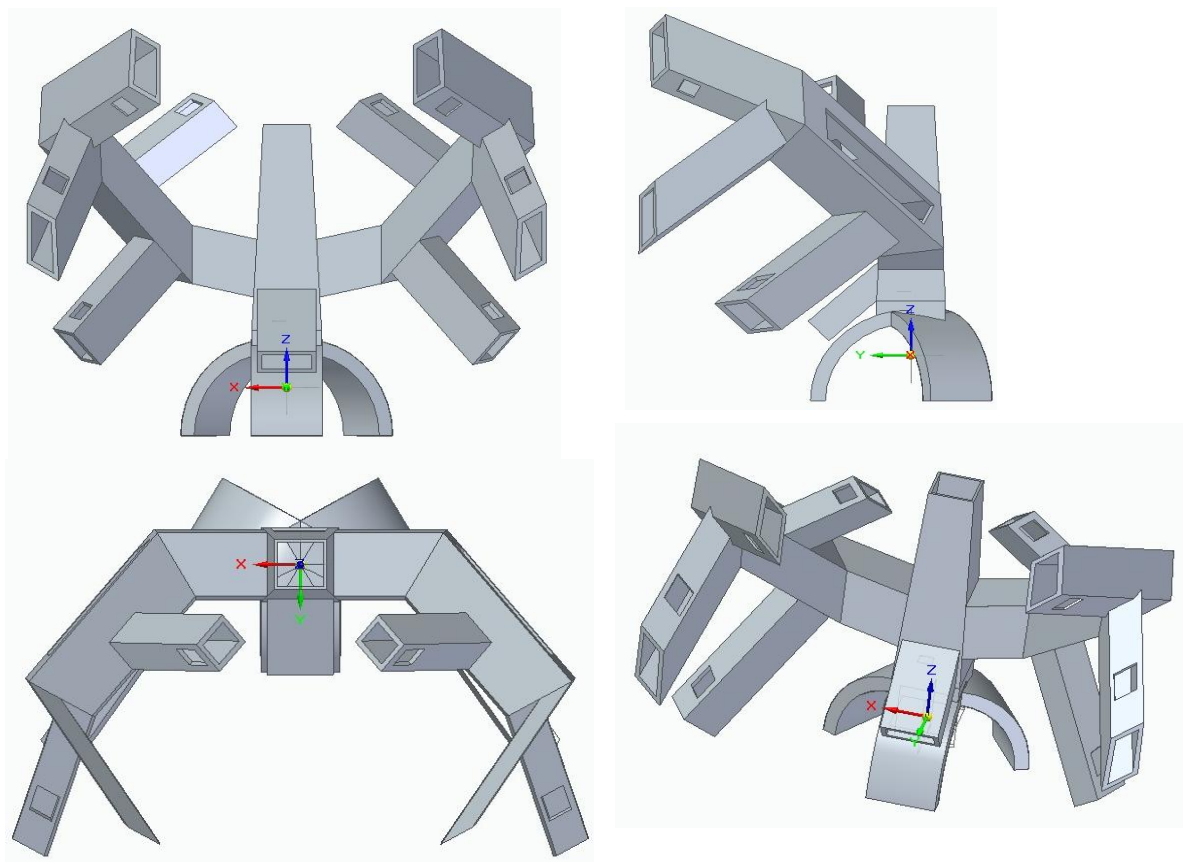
Alzado, planta, perfil y vista 3D de la segunda versión de la estructura.
